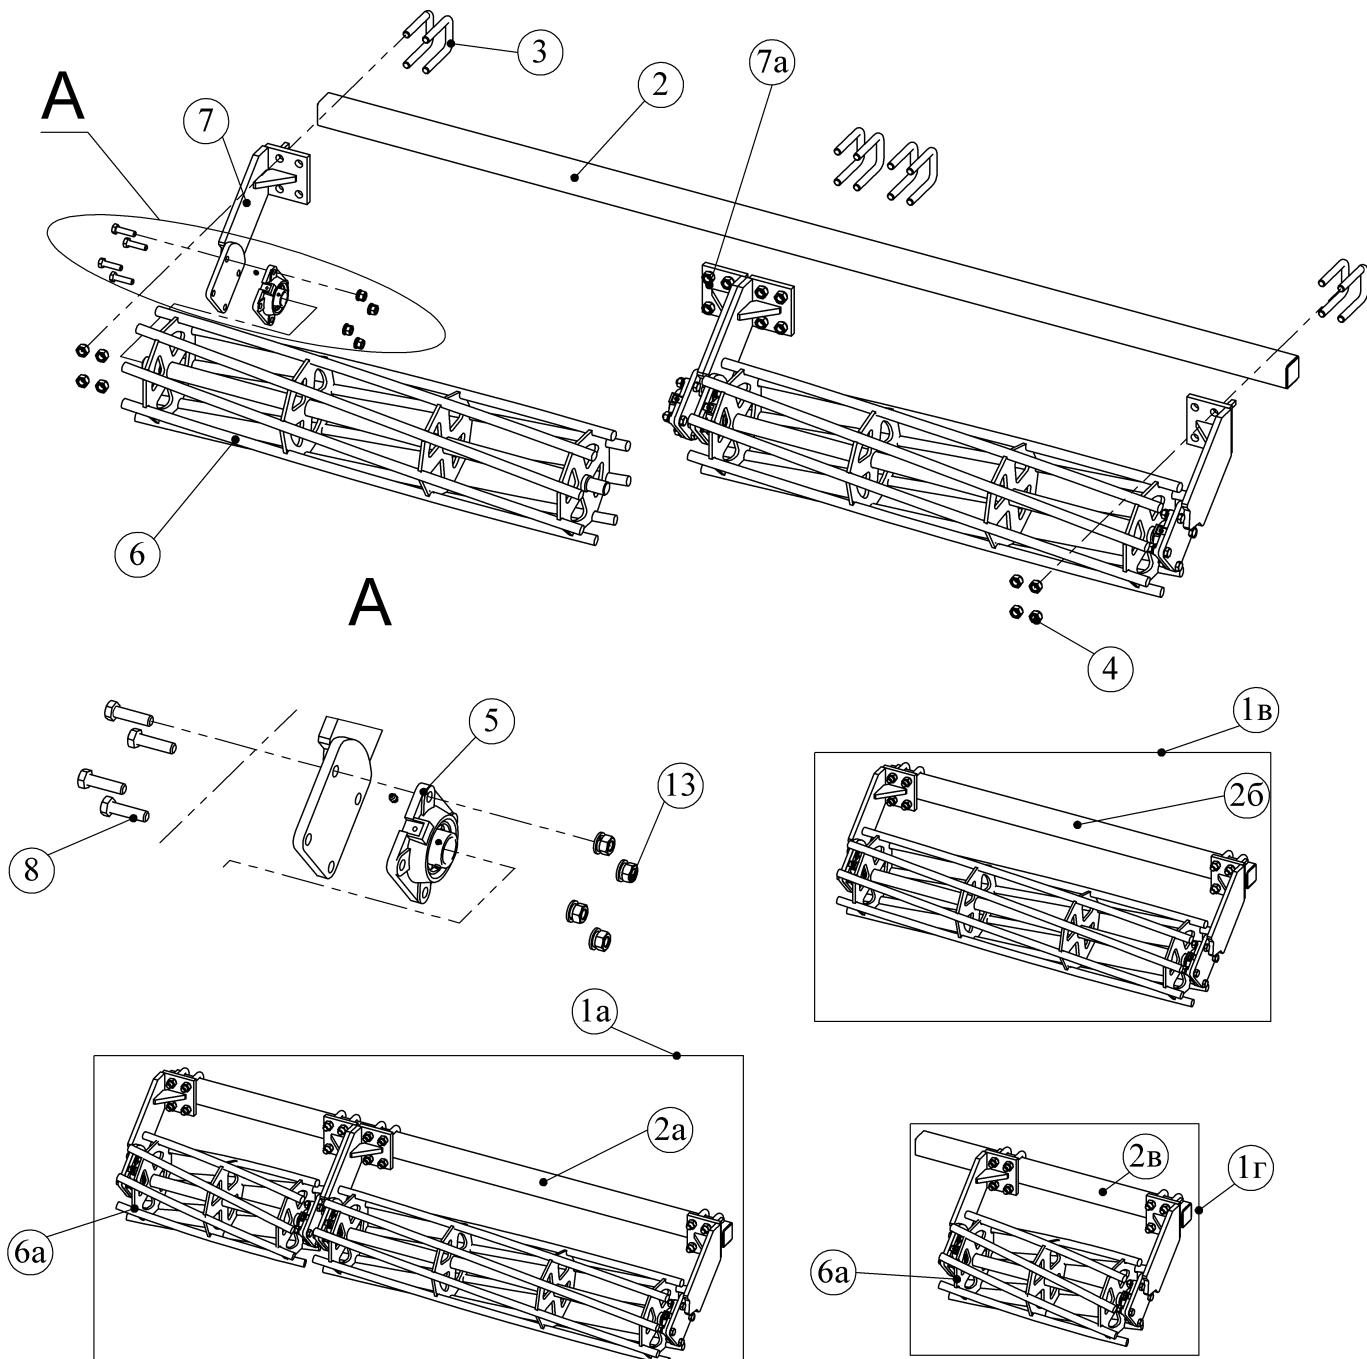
Комбинированные катки нового образца, подшипник на кронштейне катка.
